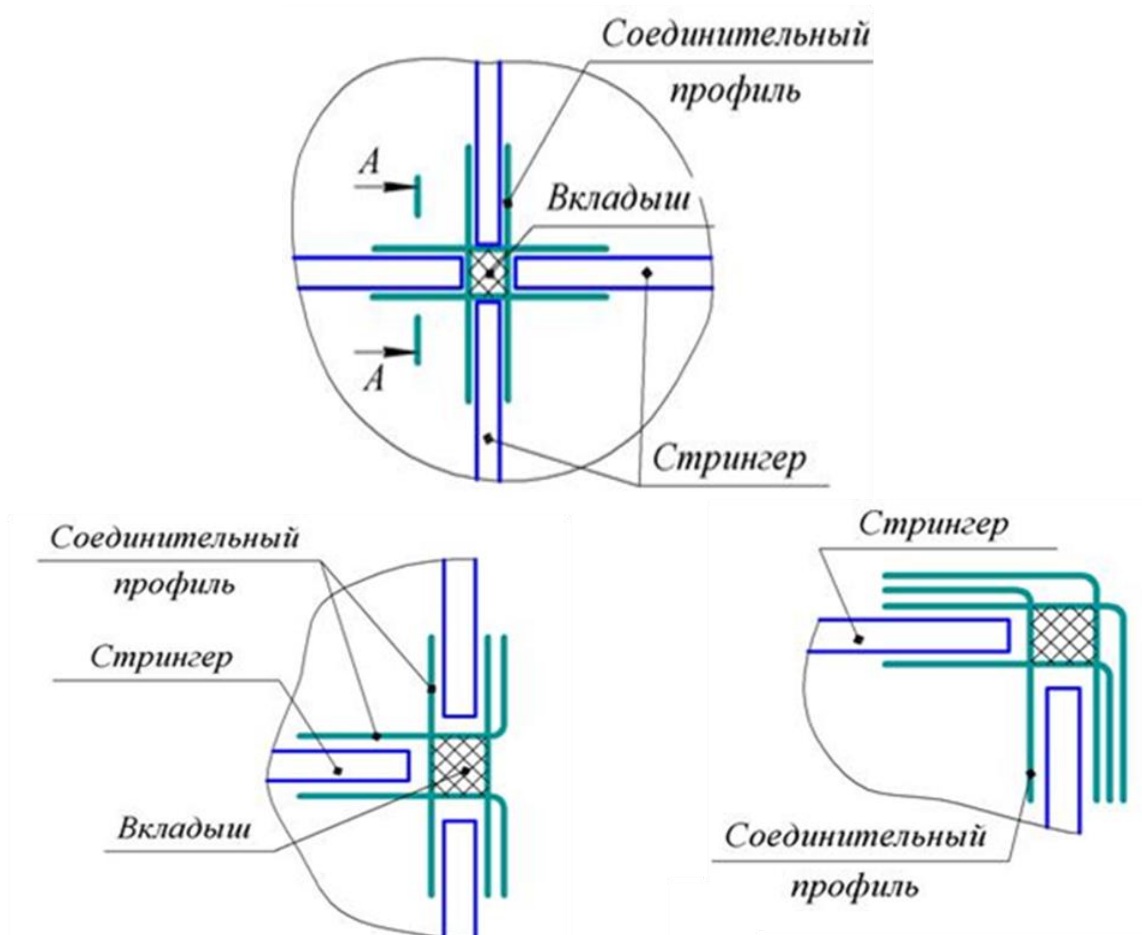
Использование специальных соединительных профилей для соединения дискретных продольных и поперечных ребер, которые изготавливаются отдельно
